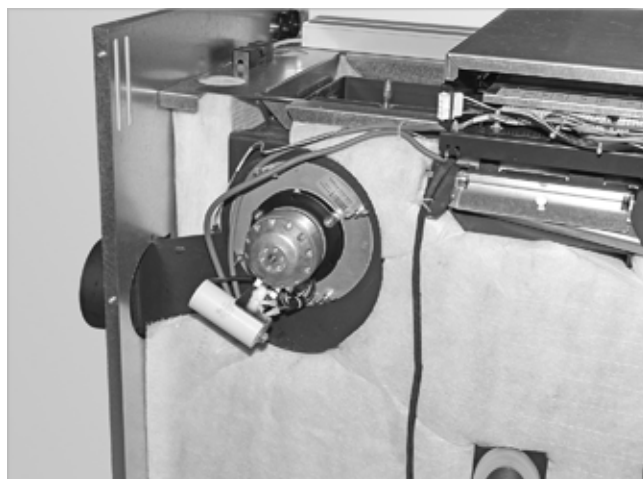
Abgasgebläse um 90° verdreht anschrauben
